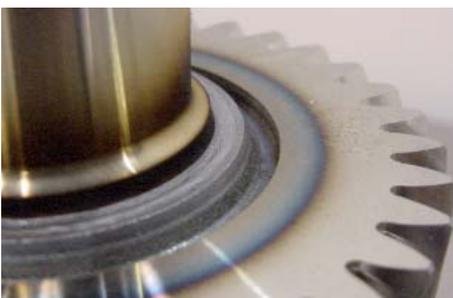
Einsatzgehärtete Verzahnung in Schweißnahtnähe
